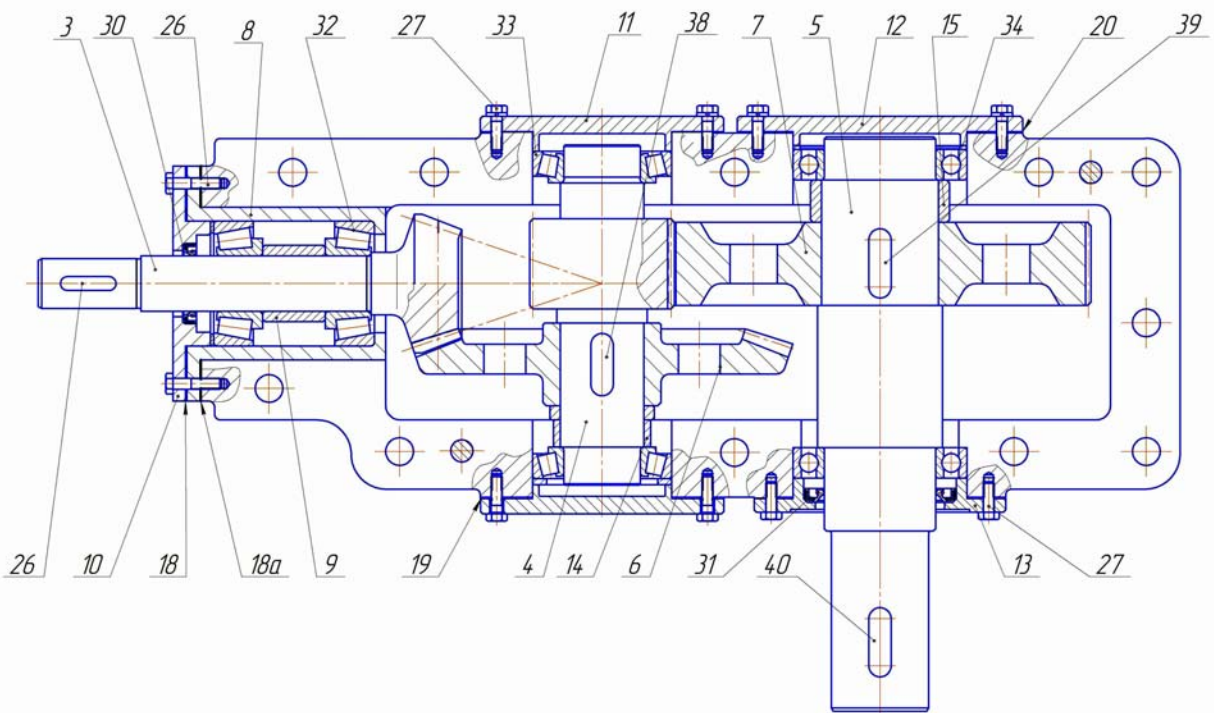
Общий вид коническо-цилиндрического редуктора
